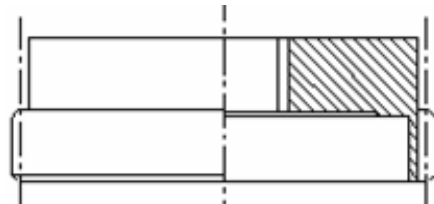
Deneysel setinin montaj çizimi. (Assembly sketch of experimental setup)
